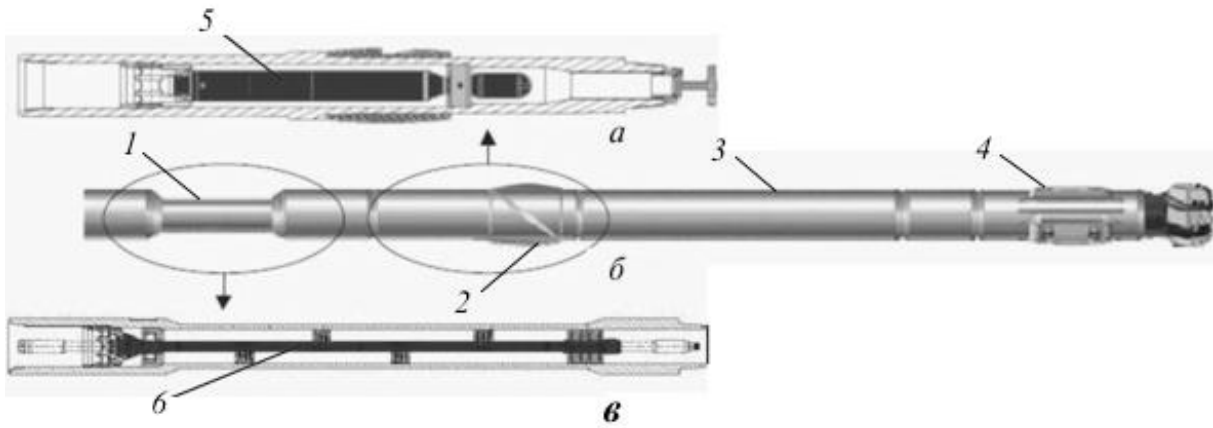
Загальний (схематичний) вигляд РКС, Power Drive компанії «Schlumberger»
